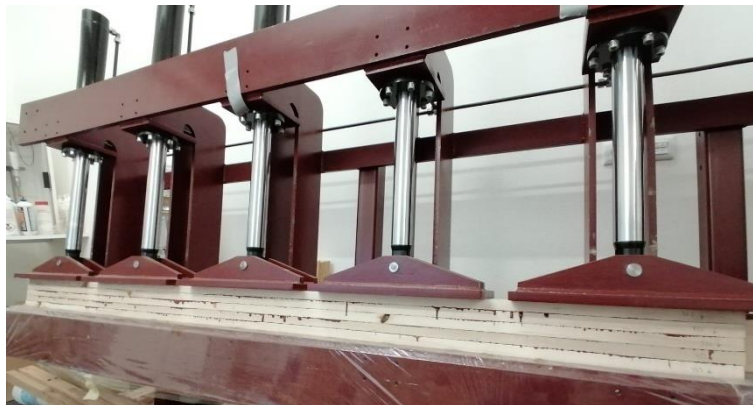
Fase de pressão na colagem de uma viga de Choupo.
